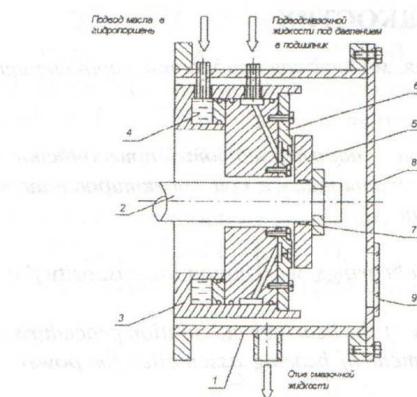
Испытательная камера: 1 - кожух, 2 - ротор, 3 - обойма, 4 - гидроцилиндр, 5 - упорный диск, 6 - подшипник, 7 - допускная лента, 8 - крышка, 9 - смотровое стекло
